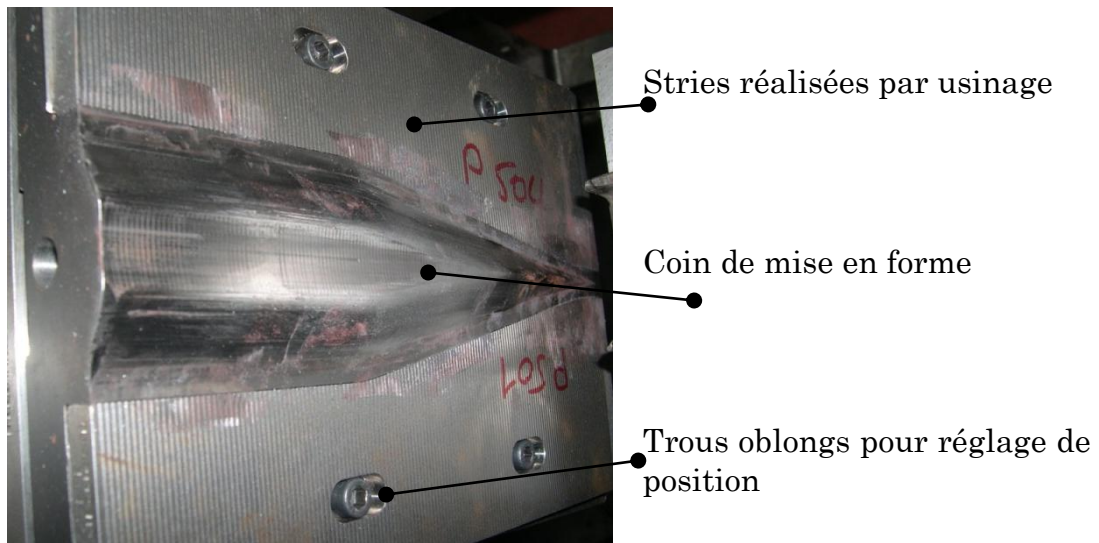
Vue de la matrice simple réduction de diamètre équipée de plaques amovibles striées pour le laminage transversal de préformes type 9004 [THESE]
